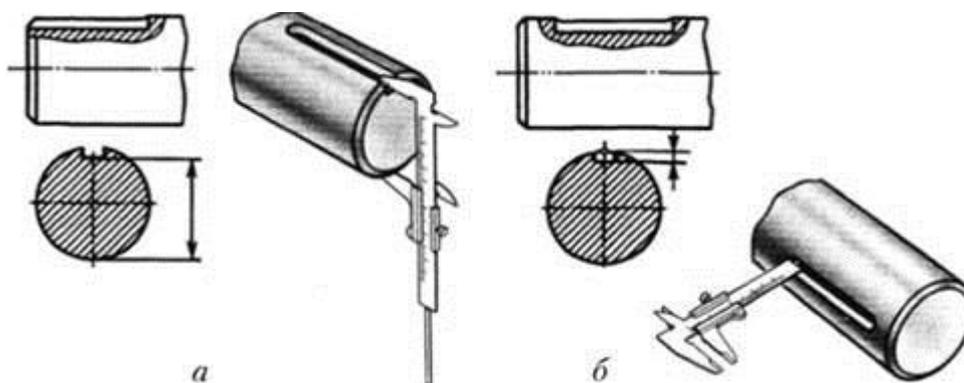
Нанесение размера глубины шпоночного паза:
